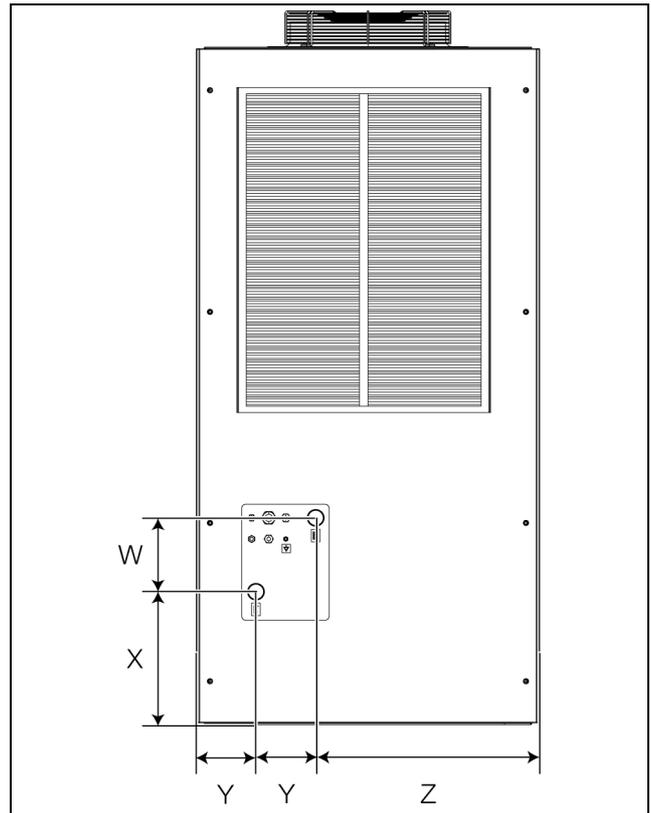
Abmessungen (Versorgungsanschlüsse) Rückseite ohne Sockel (abgebildet 3335.790)
